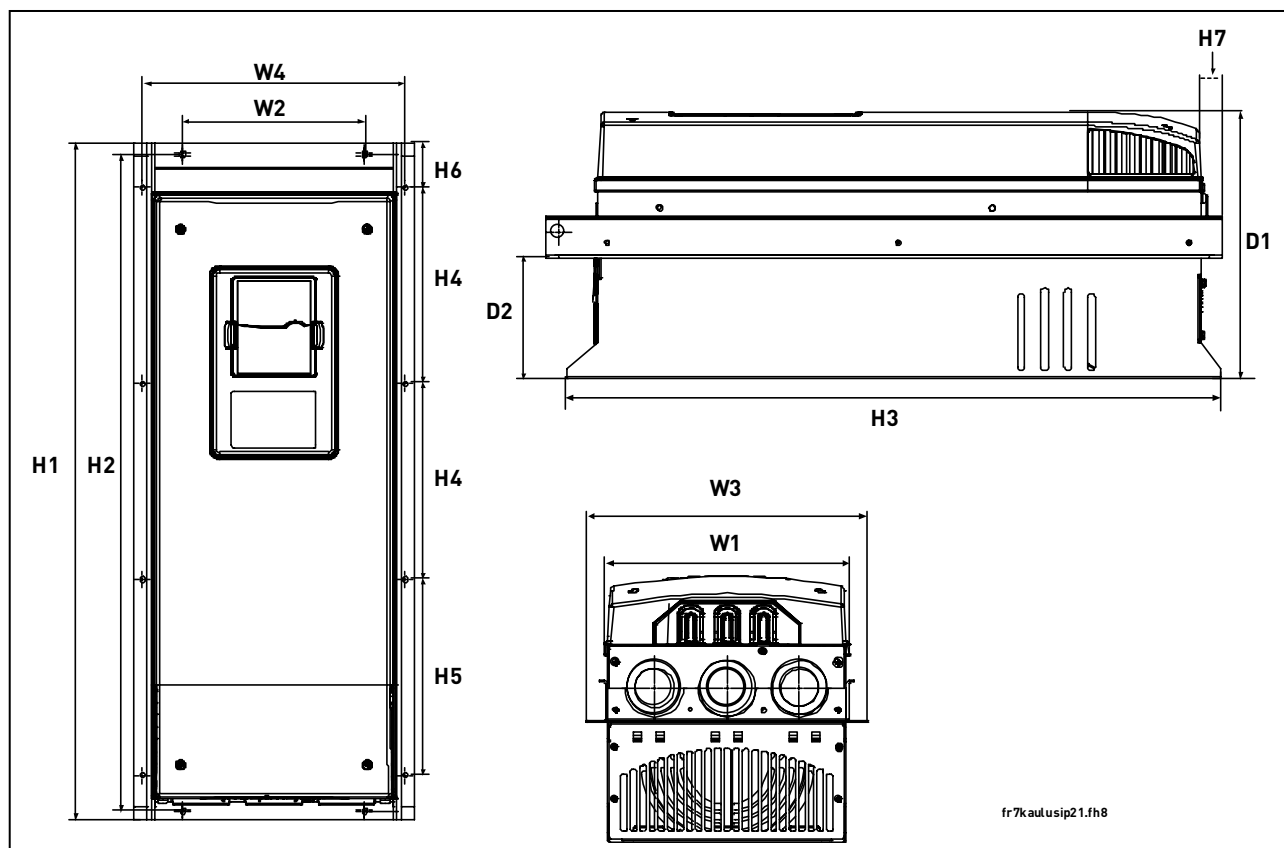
Габариты преобразователей частоты фланцевого исполнения, типоразмеры FR7 и FR8
